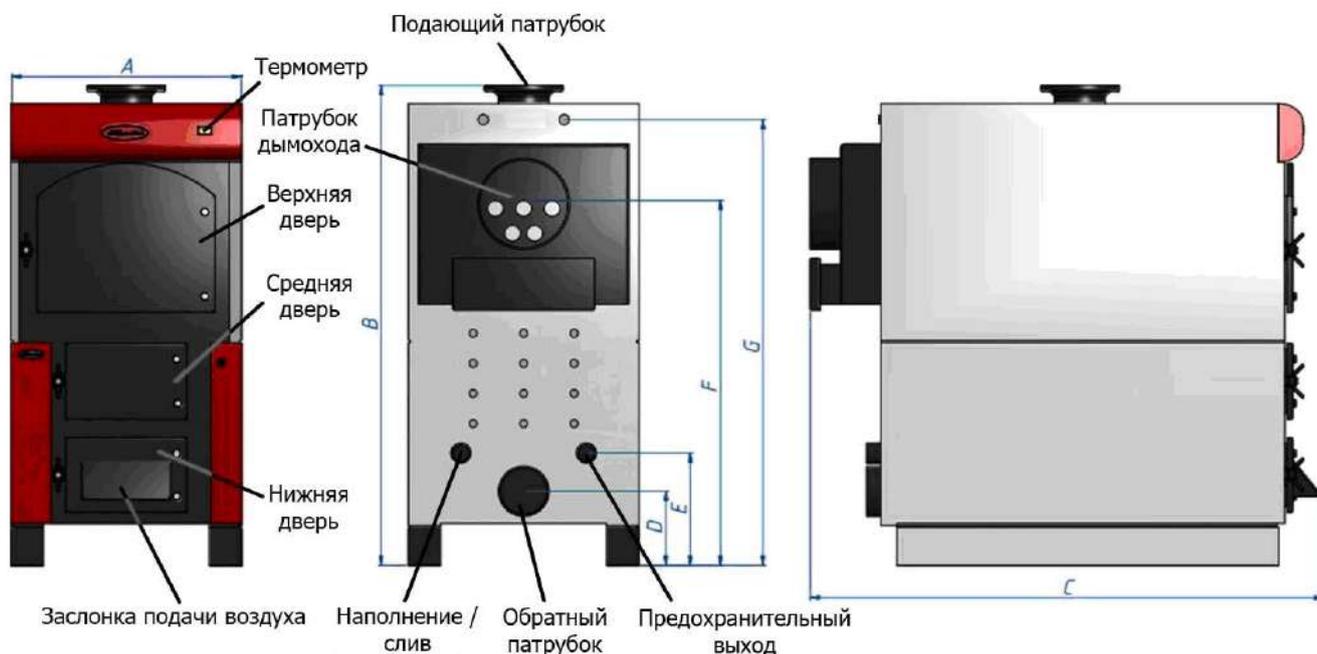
Вид и размеры котла WIRBEL™ ECO TKS 125÷550 кВт
